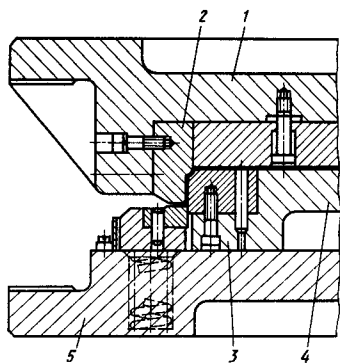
Штампы для правки (калибровки) ступенчатой детали
